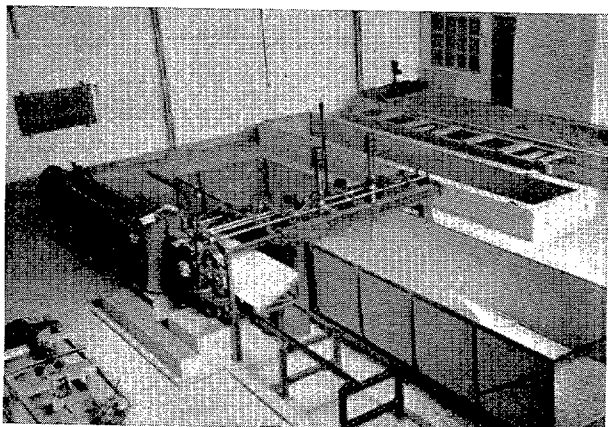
Vista de conjunto de la máquina fresadora tallando un modelo.
